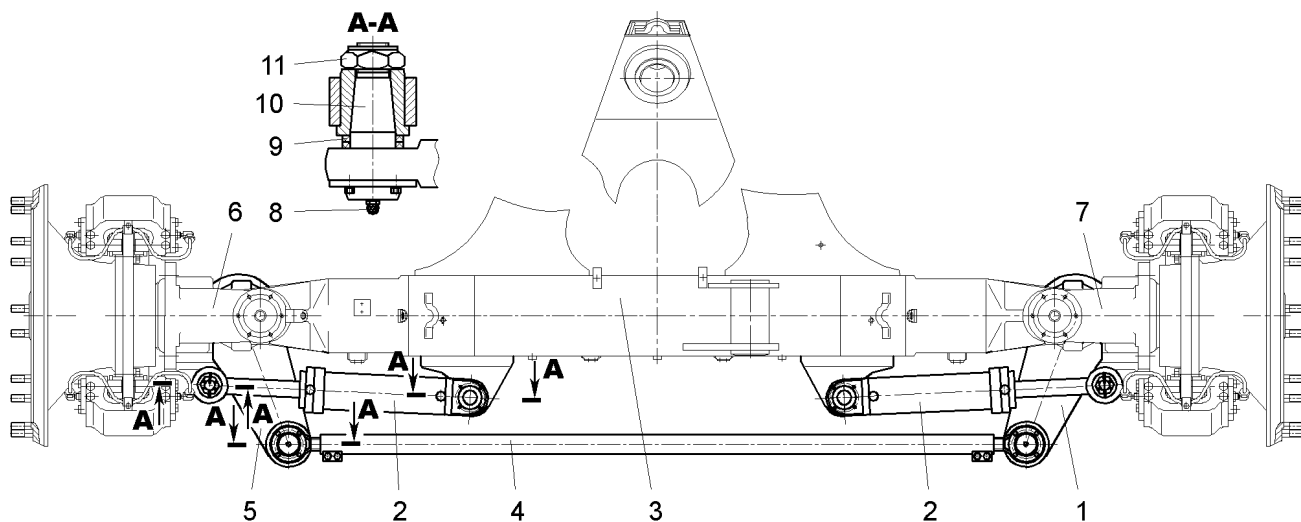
Установка цилиндра поворота и тяги рулевой трапеции:
